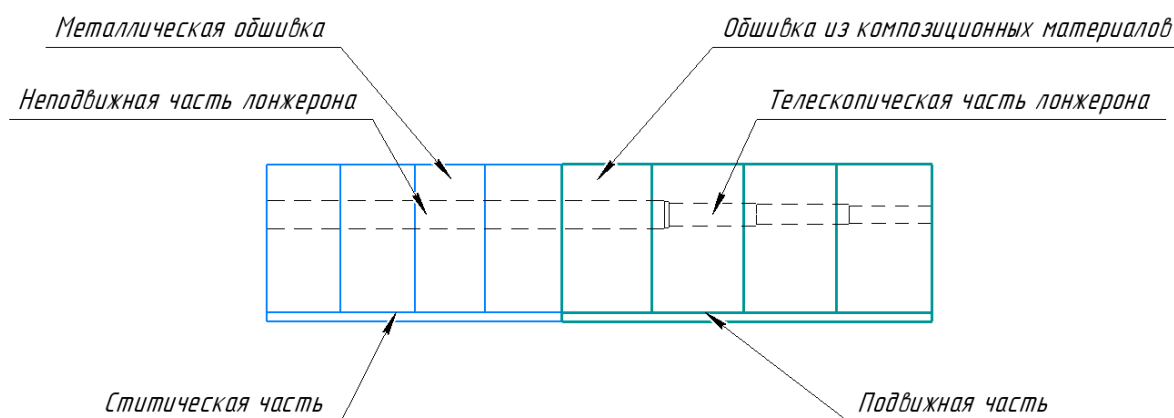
Схема конструкции консоли крыла с деформирующейся композитной обшивкой
